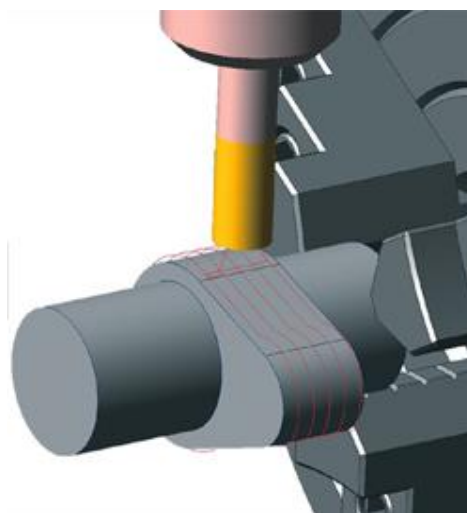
Obrábění na 4osém soustružnickém obráběcím centru (typ XYZC) [20]
